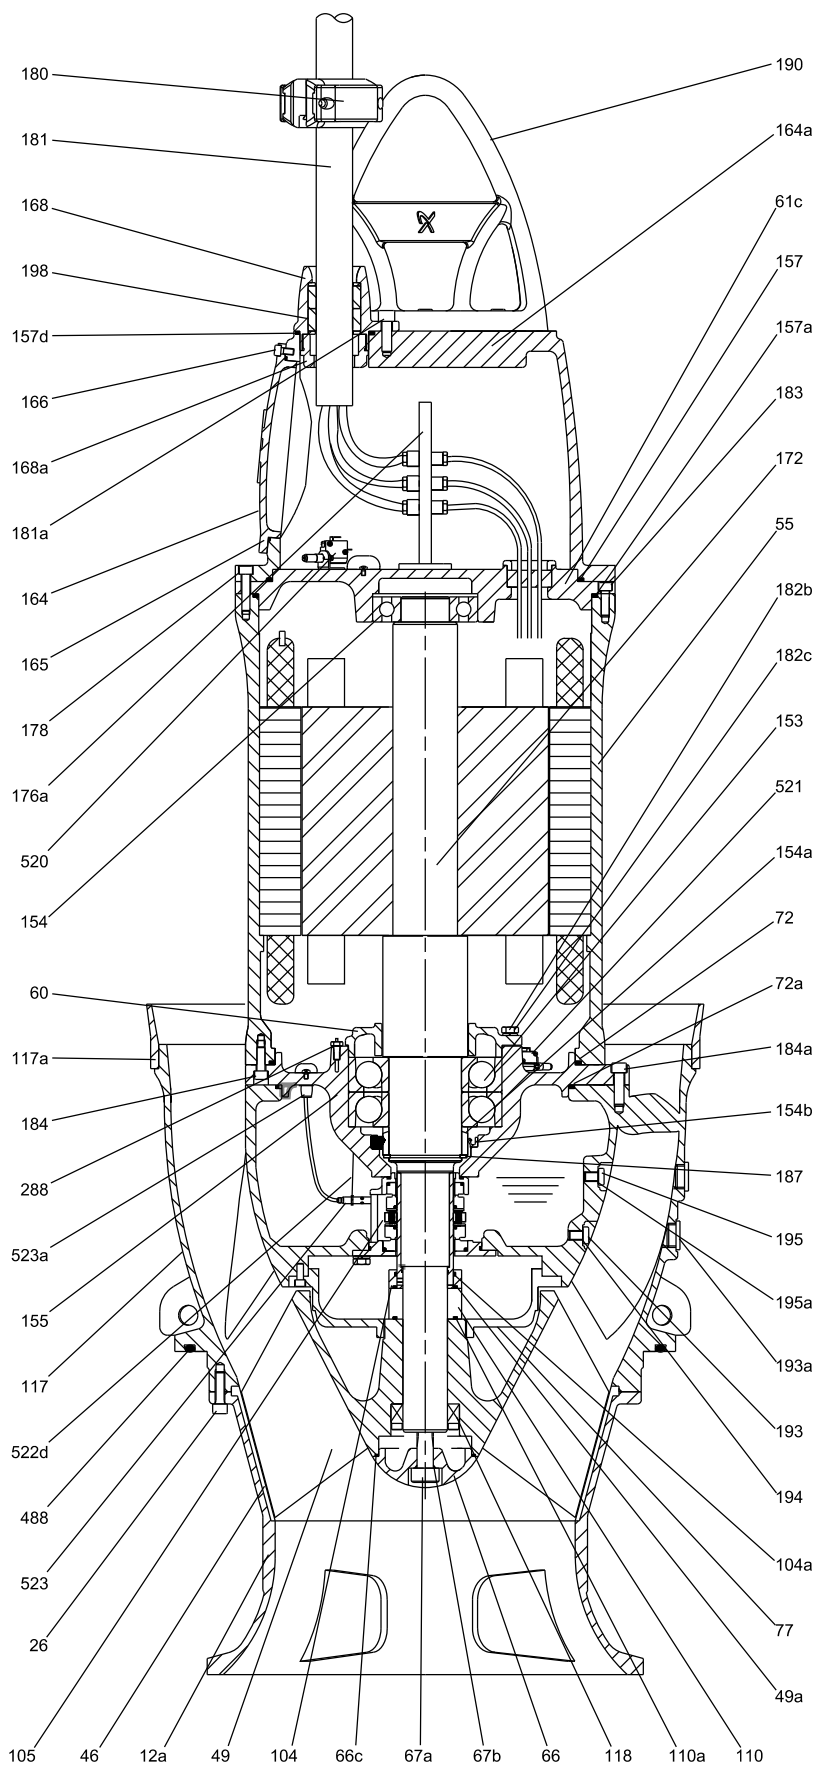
Чертеж в разрезе, KWM, обсадная труба диаметром 600-700
